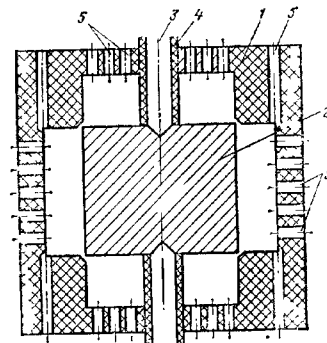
Приспособление для одновременного хромирования торцов и боковой поверхности цилиндрической детали:
